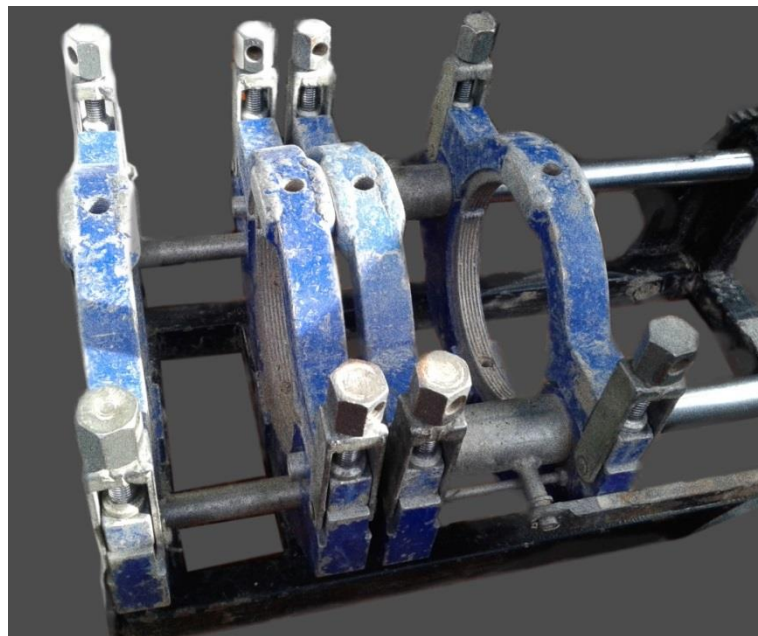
Обладнання для центрування та закріплення труб при зварюванні
